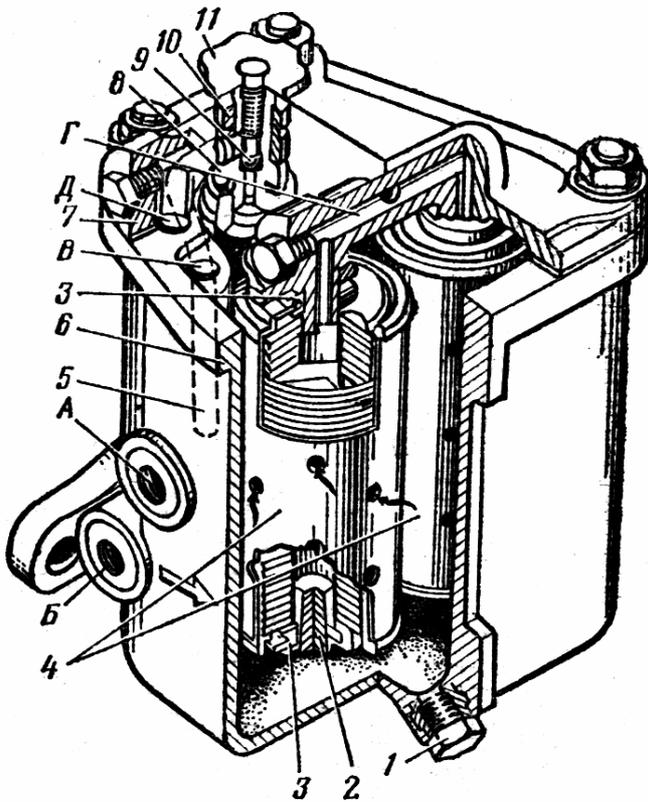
Фильтр тонкой очистки топлива двигателя Д-240:
